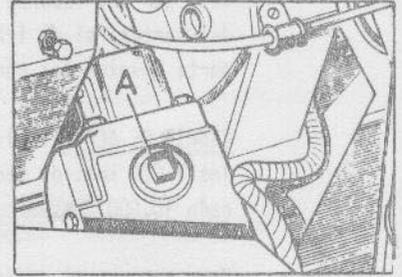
Tapón de llenado de la caja de engranajes de la dirección
